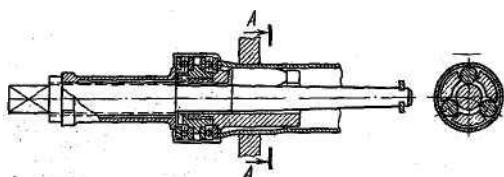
Вальцовки крепежные ВК. Общий вид
